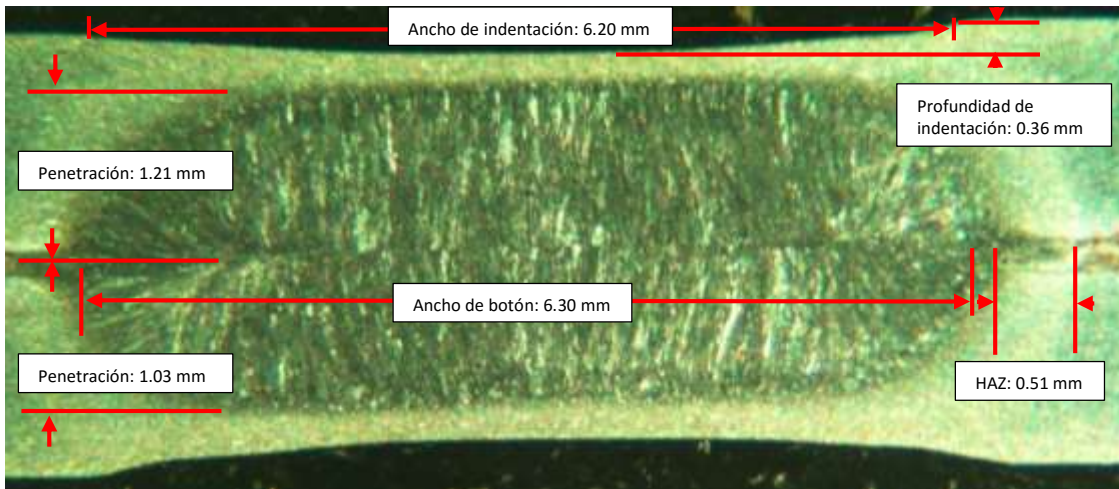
Mediciones realizadas en el botón de soldadura número 8.
